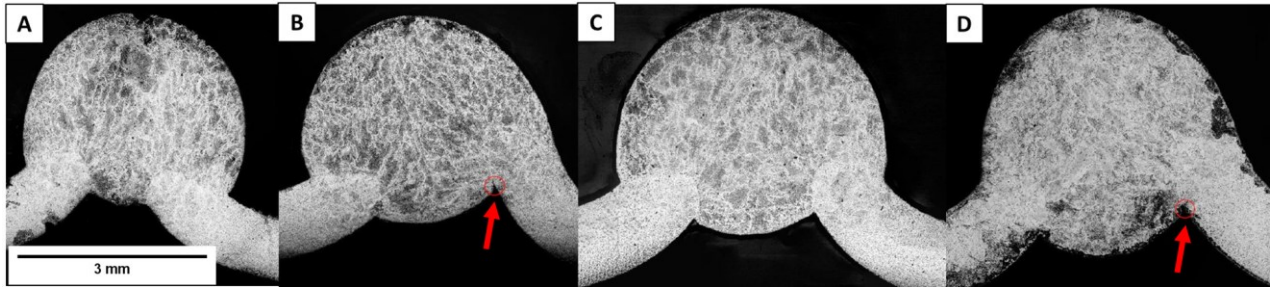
Aumento de 50x soldagem GMAW. a) Condição de soldagem 1. b) Condição de soldagem 2. c) Condição de soldagem 6. d) Condição de soldagem 7 (Próprio autor)
